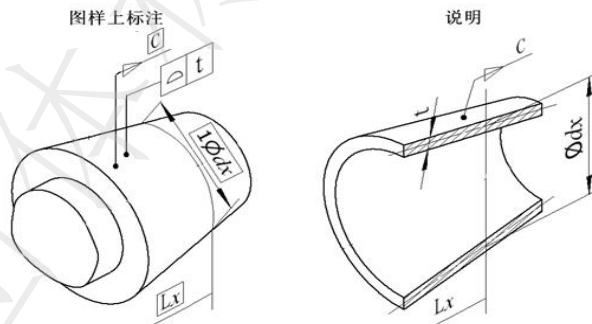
给定圆锥轴向位置的圆锥公差注法
